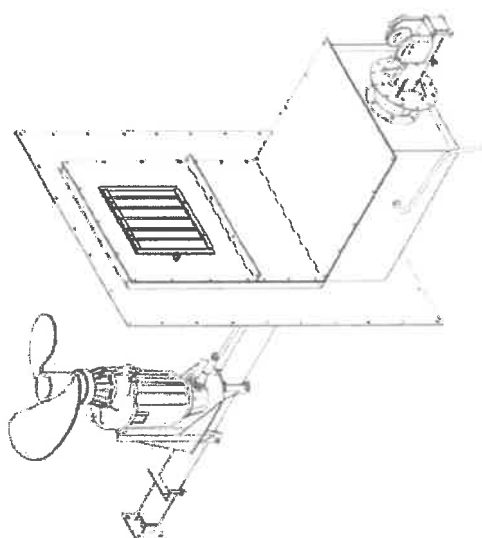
Dispositif suspendu de type ZZH-BP destiné aux cuves fermées en béton, montage au plafond.
